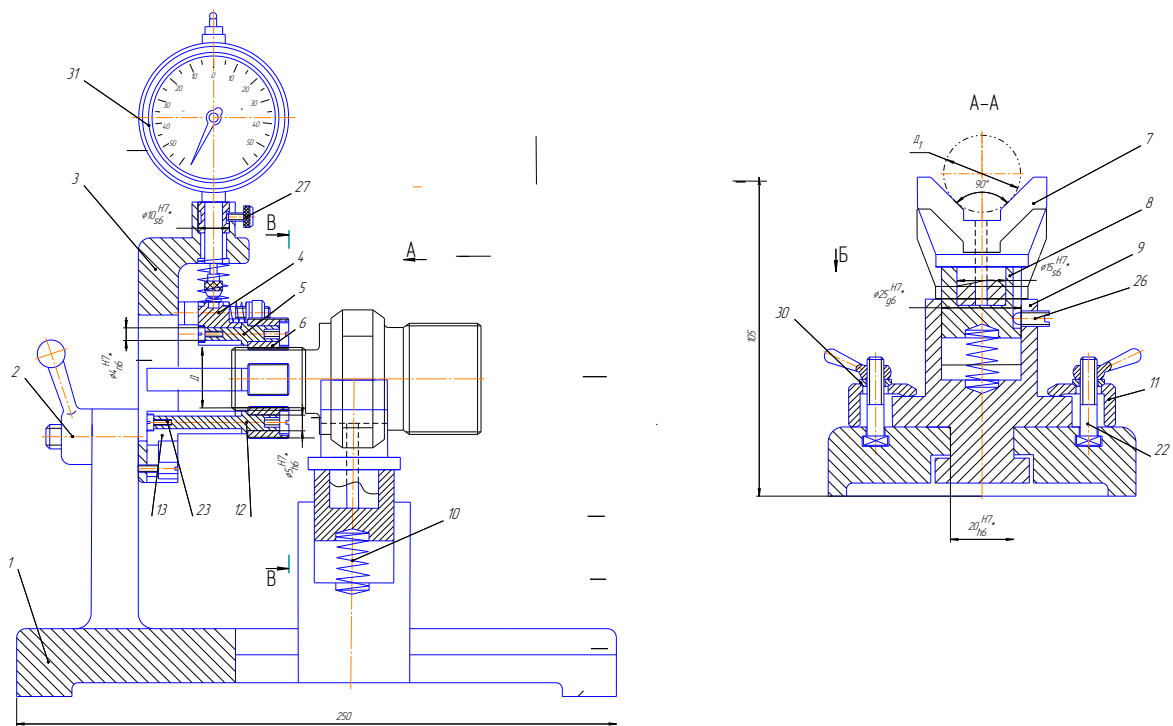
Приспособление для контроля метрической резьбы
